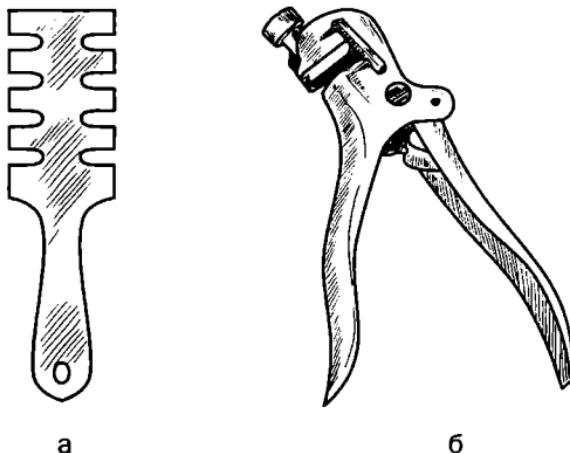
Инструменты для разводки ручных пил: а — разводка с упорами; б — универсальная разводка
